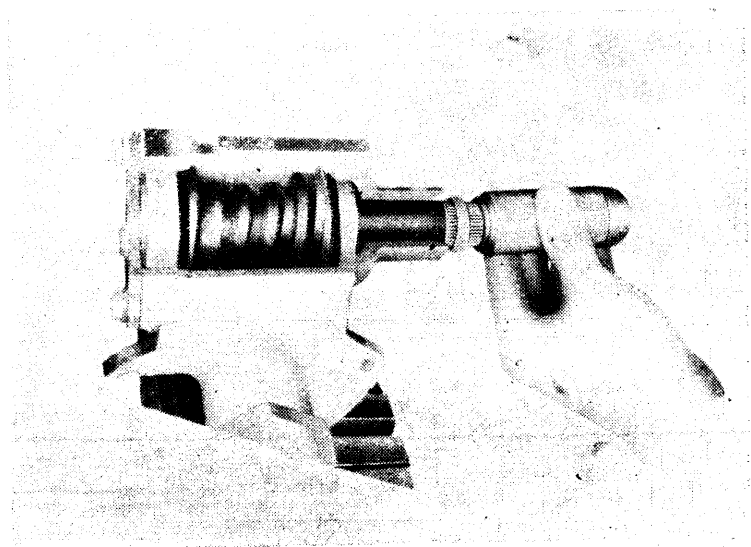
Einpressen der Korkdichtung in das Gehäuse des Dichtringes mittels Vorrichtung D-58.
